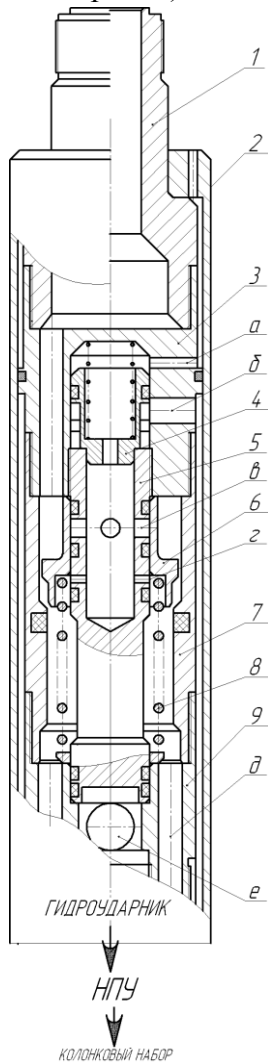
Схематический чертеж усовершенствованного ВПУ
